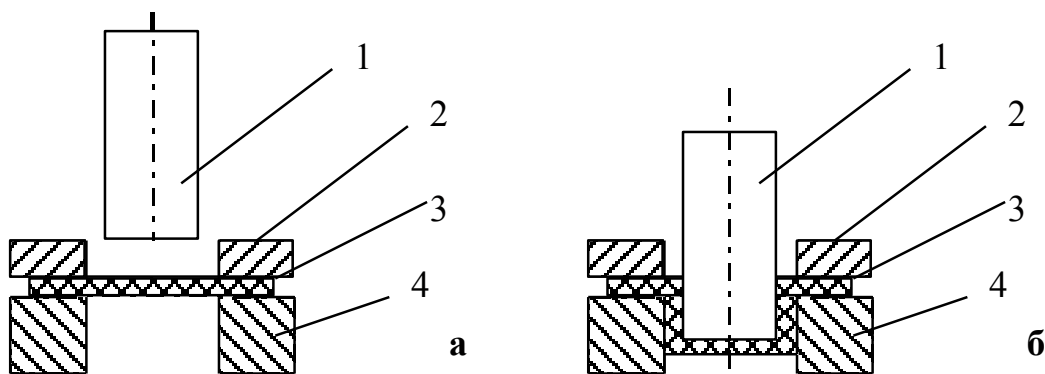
Схема глубокой вытяжки: а - положение до деформации; б - положение после деформации; 1 - пуансон; 2 - прижим; 3 - заготовка; 4 - матрица
